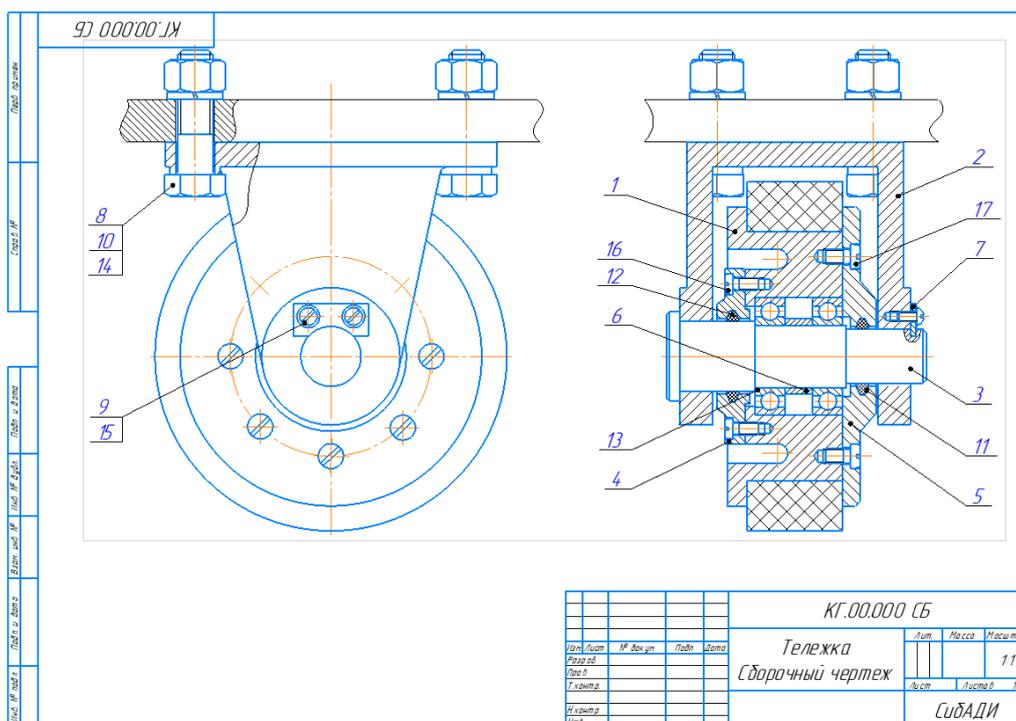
Сборочный чертёж КГ.00.000 СБ – Тележка
